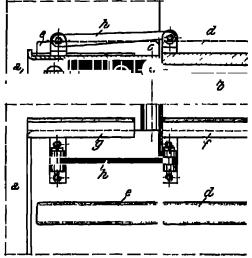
Zwangläufige Steuerung des hinteren Lauf schilltens durch einen Lenker. a Gehäuse, b Lauf boden, o gemeinsames Gelenk, d verdere lange Lauf schleue mit Pührung J. a hintere kurze Laufschleumit Pührungschlenen g, h Lanker
